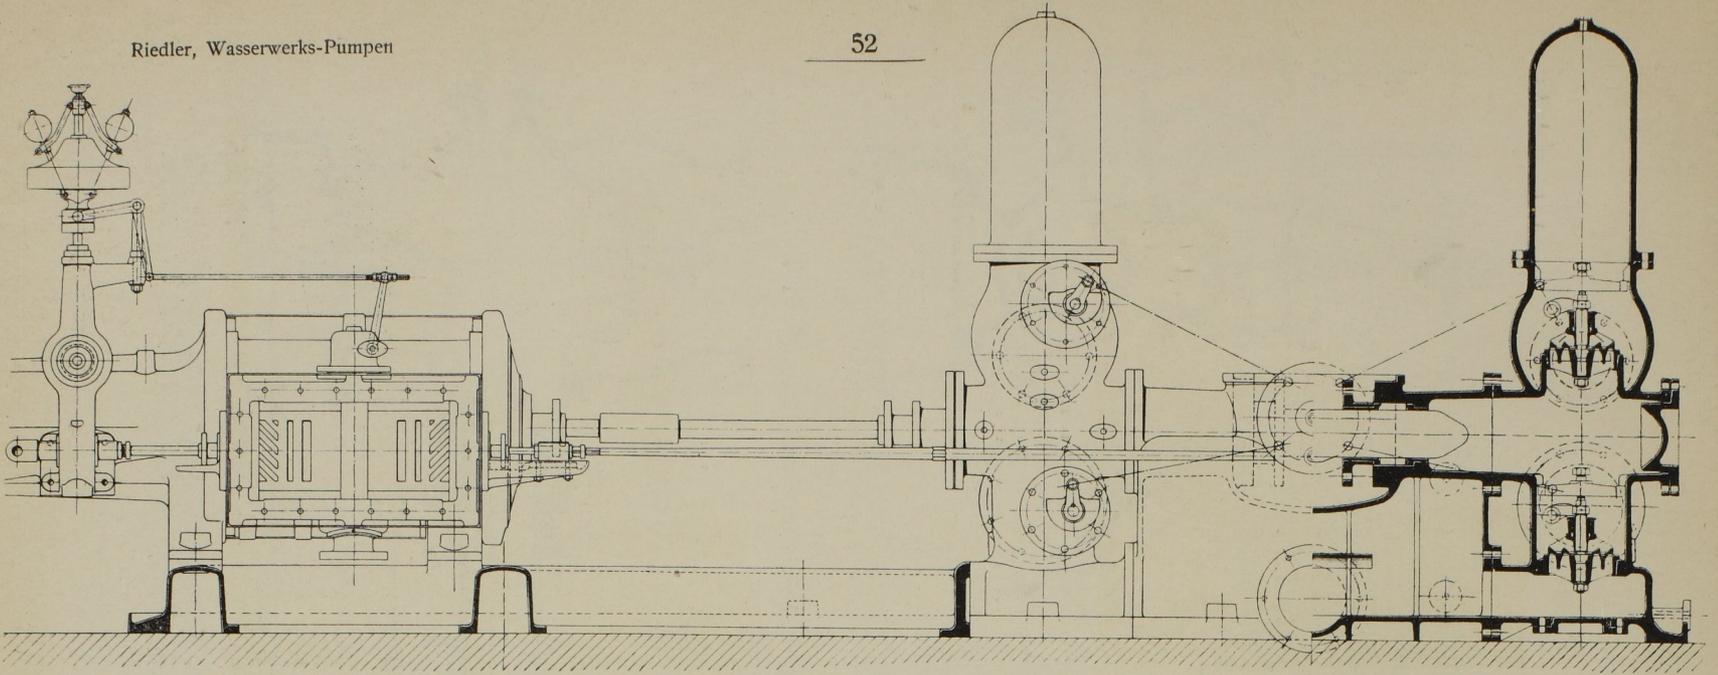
Seitenansicht der Pumpmaschine. Masst. 1:25.
